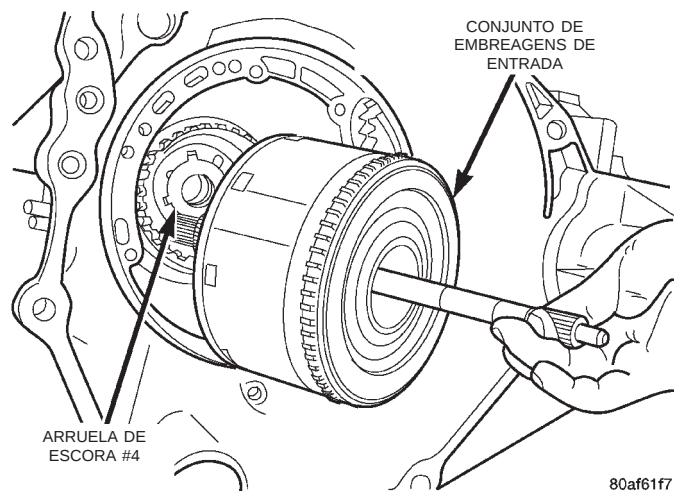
Instalação do Conjunto de Embreagens de Entrada
